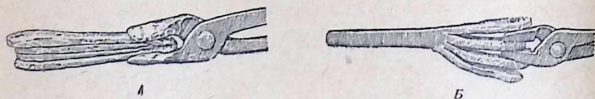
Сварка пакетом четырех половин двух подков: А—перед закладкой в горн; Б—сваренный конец.
